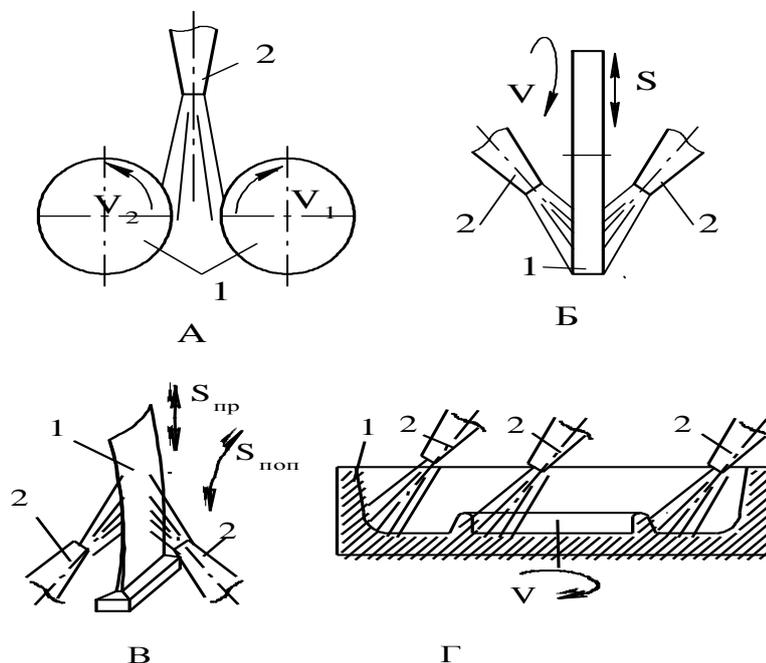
Схемы струйной обработки: А – двух цилиндрических заготовок; Б – диска; В – лопатки компрессора; Г – пресс-формы; 1 – обрабатываемая заготовка; 2 – струйный аппарат
